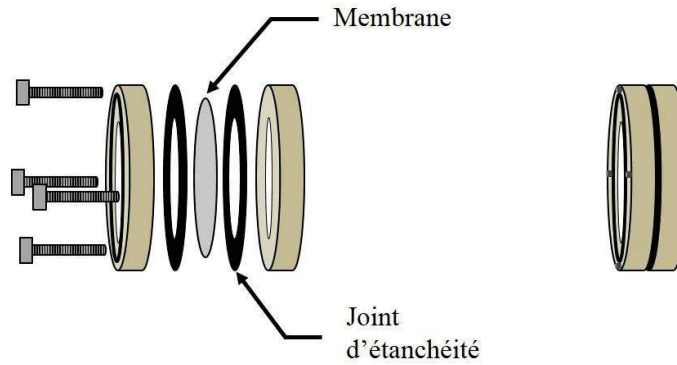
Schémas d'assemblage des blocs du milieu (gauche) vue éclatée et (droite) vue assemblée.
